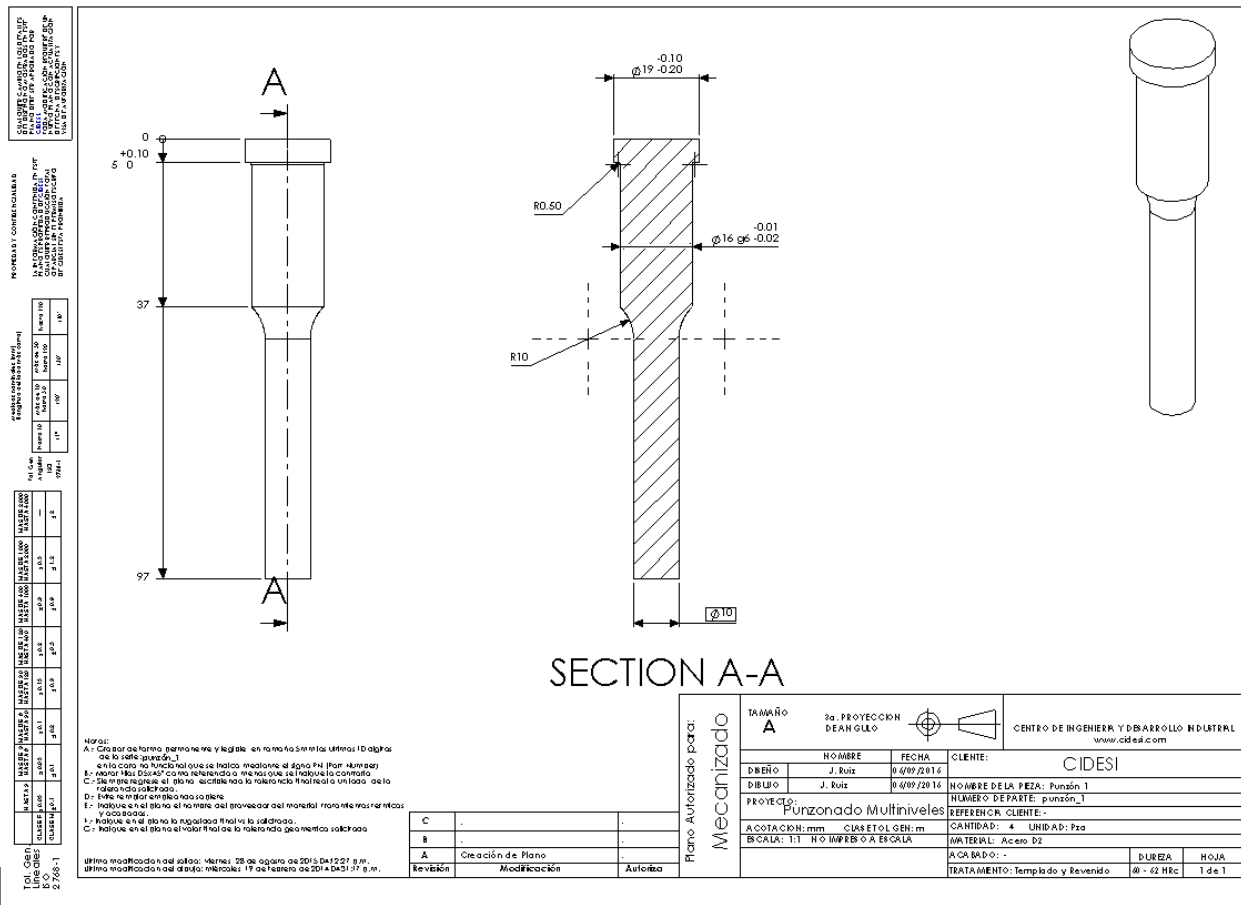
Plano de manufactura de punzón. Elaboración propia, 2014.
